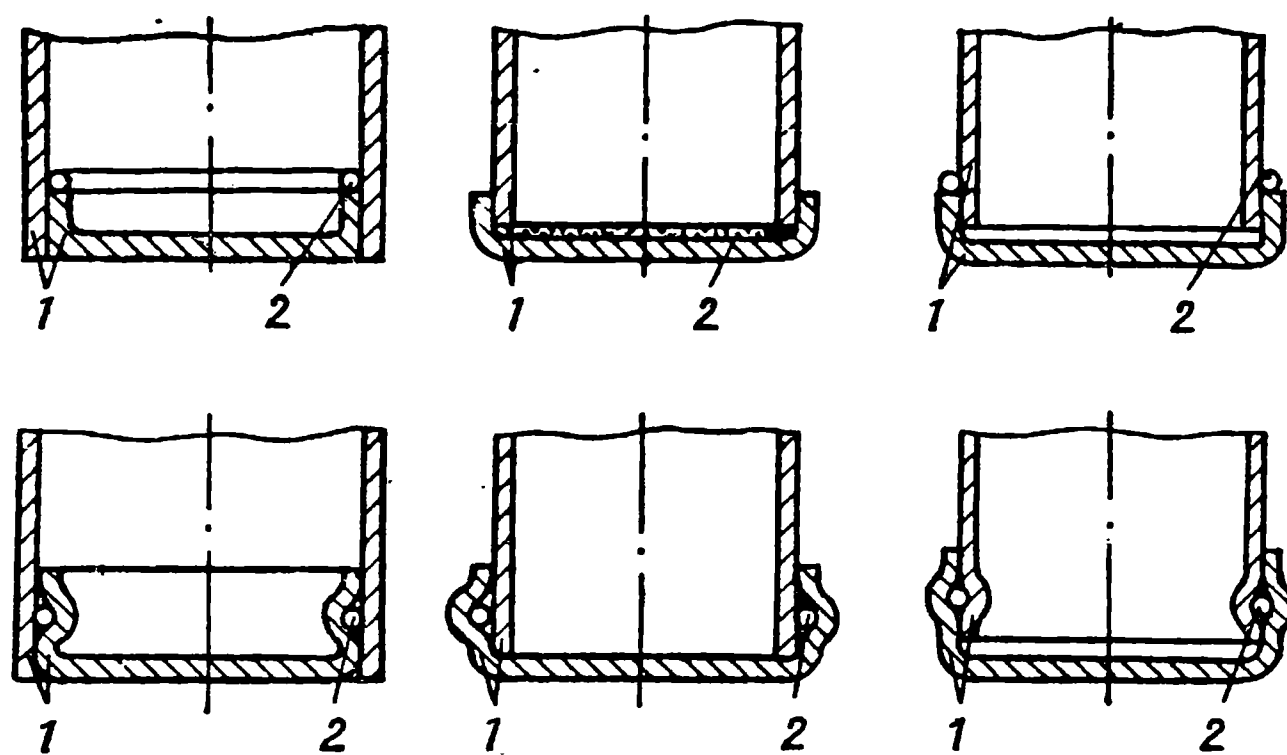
Способы размещения припоя в соединениях из штампованных деталей:
